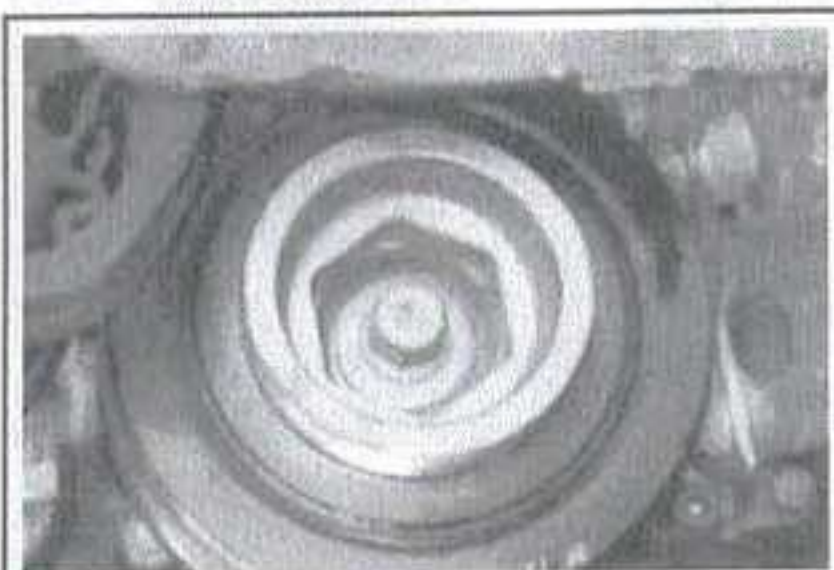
Для откручивания болта на шкиве коленчатого вала отлито 50 мм углубление шестигранной формы под инструмент для фиксации шкива
